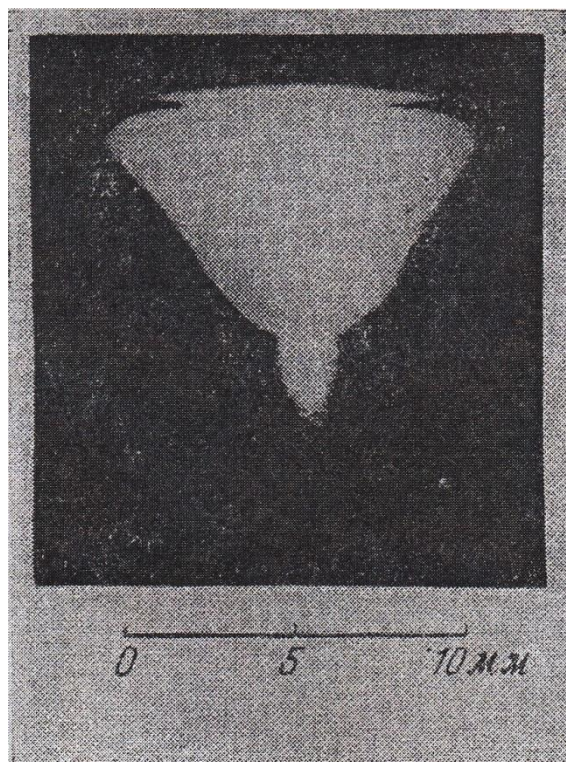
Сварочная дуга, горящая в аргоне[21]
